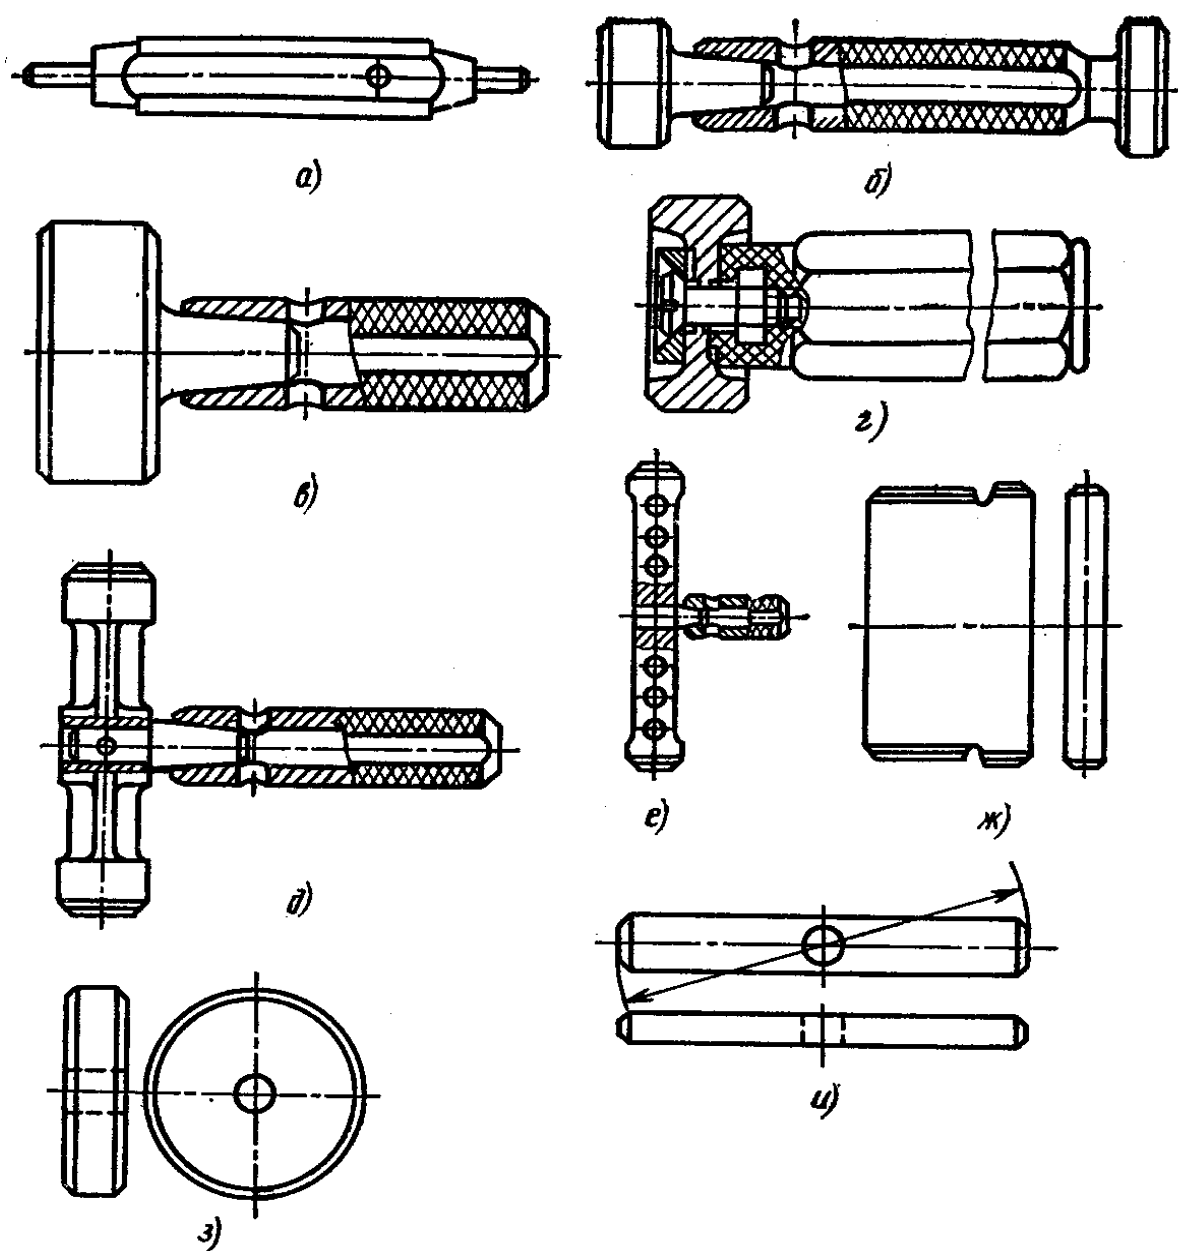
Основные типы калибров-пробок для контроля отверстий и контрольные калибры к скобам:
